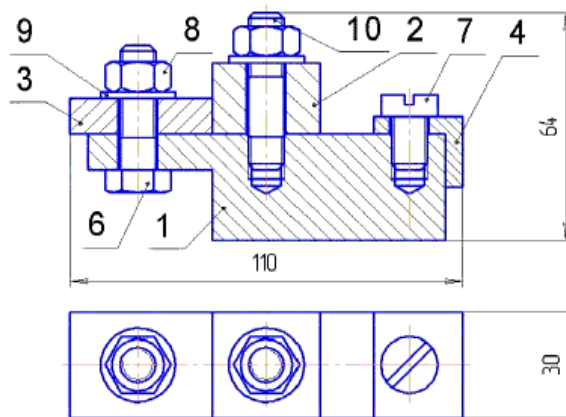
Пример конструктивных изображений резьбовых соединений
